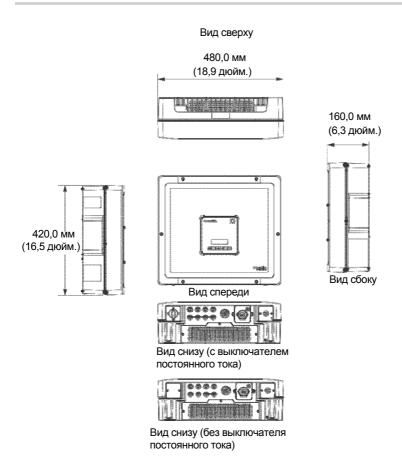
Внешний вид и размеры инвертора Conext RL 4000E-S/ 4000 E
